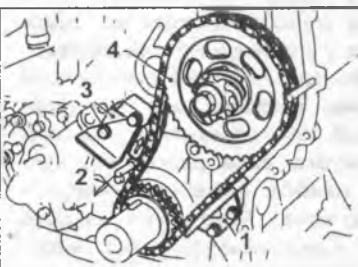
1. Направляющая. 2. Звездочка коленвала. 3. Натяжитель. 4. Звездочка распределителя.
